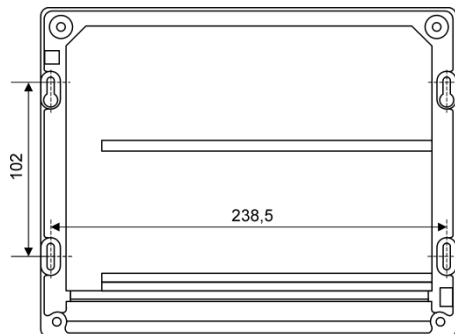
Присоединительные размеры составной части контроллера в корпусном исполнении
